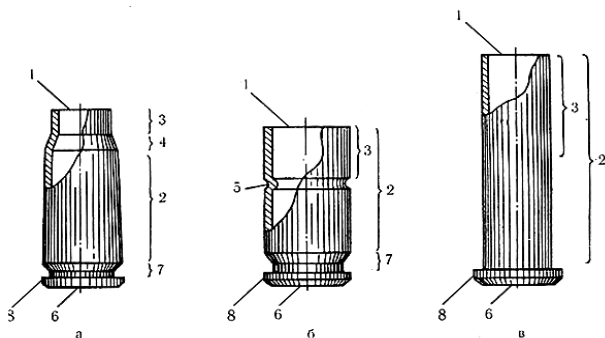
Элементы гильз (а – пистолетная гильза бутылочной формы; б – пистолетная гильза цилиндрической формы; в – винтовочная гильза цилиндрической формы). 1 – срез; 2 – корпус; 3 – дульце; 4 – скат; 5 – каннелюра; 6 – донце (дно); 7 – кольцевая проточка; 8 – фланец
